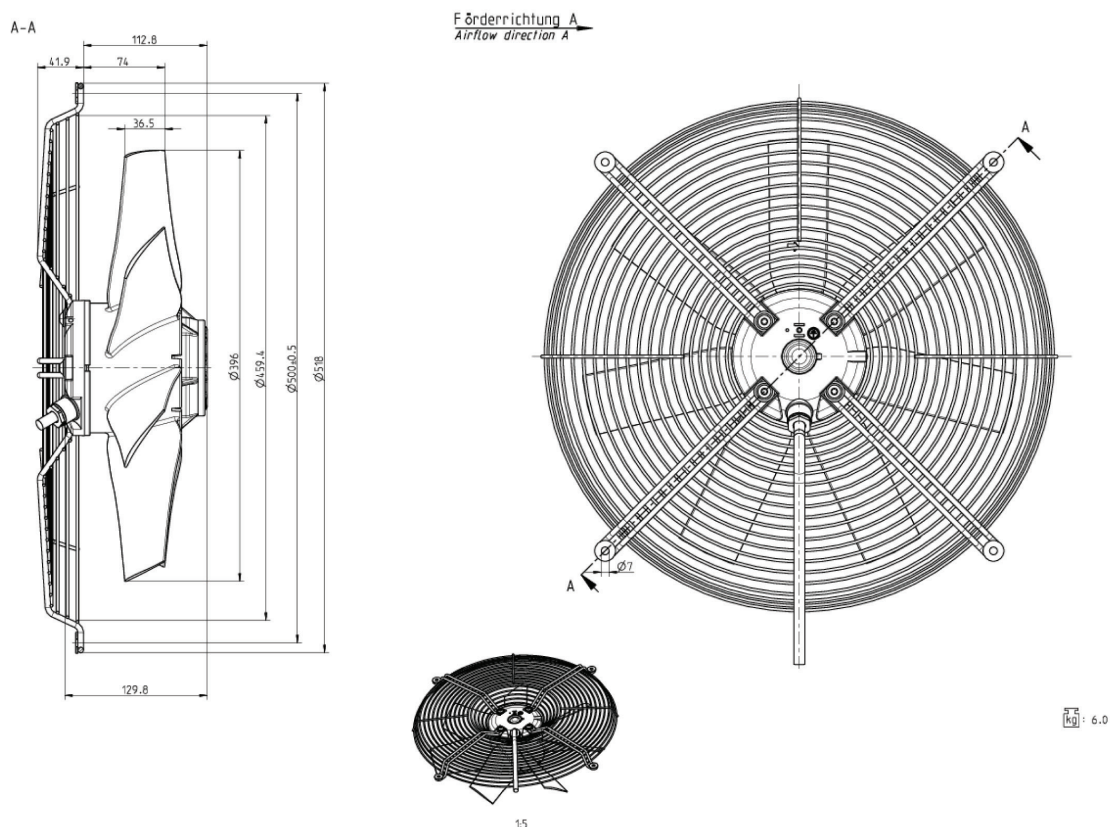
Axialventilator – Gesamtdurchmesser inkl. Befestigung 518 mm (Maße in mm)
